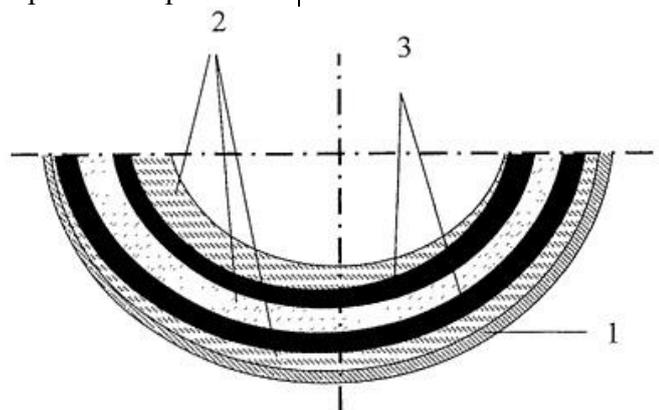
Схема древесно-металлического вкладыша подшипника скольжения: 1 - опорная втулка; 2 - проклеенные древесные слои; 3 - металлическая полоса или сетка
